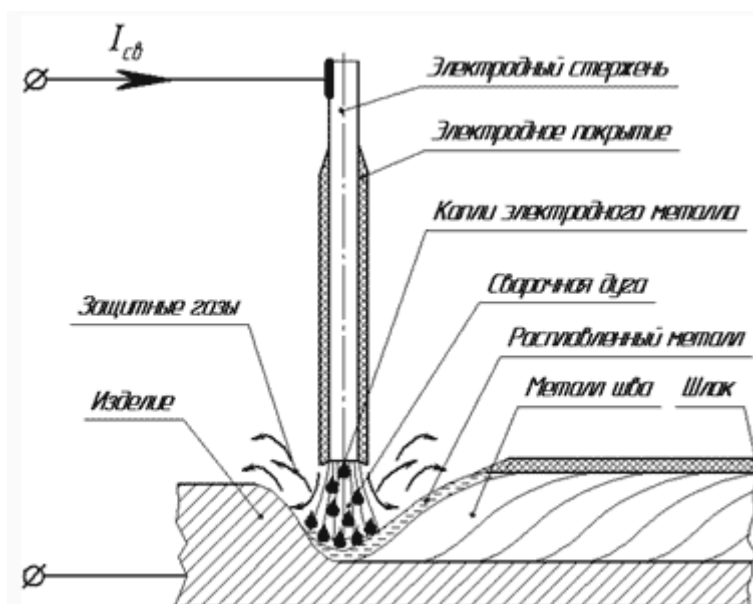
Схема сварки покрытым металлическим электродом
